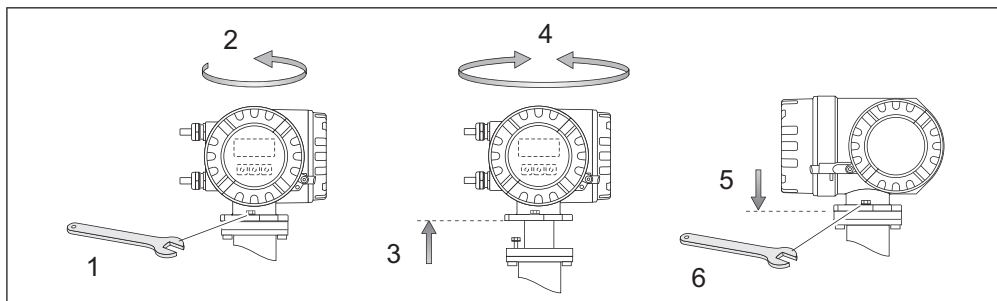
Вращение корпуса трансмиттера (алюминиевый полевой корпус)
